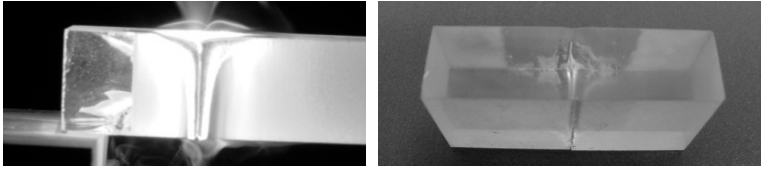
Schweißnaht bei Plattendicke $d = 20$ mm (links) und Schweißnaht bei Plattendicke $d = 5$ mm (rechts)
